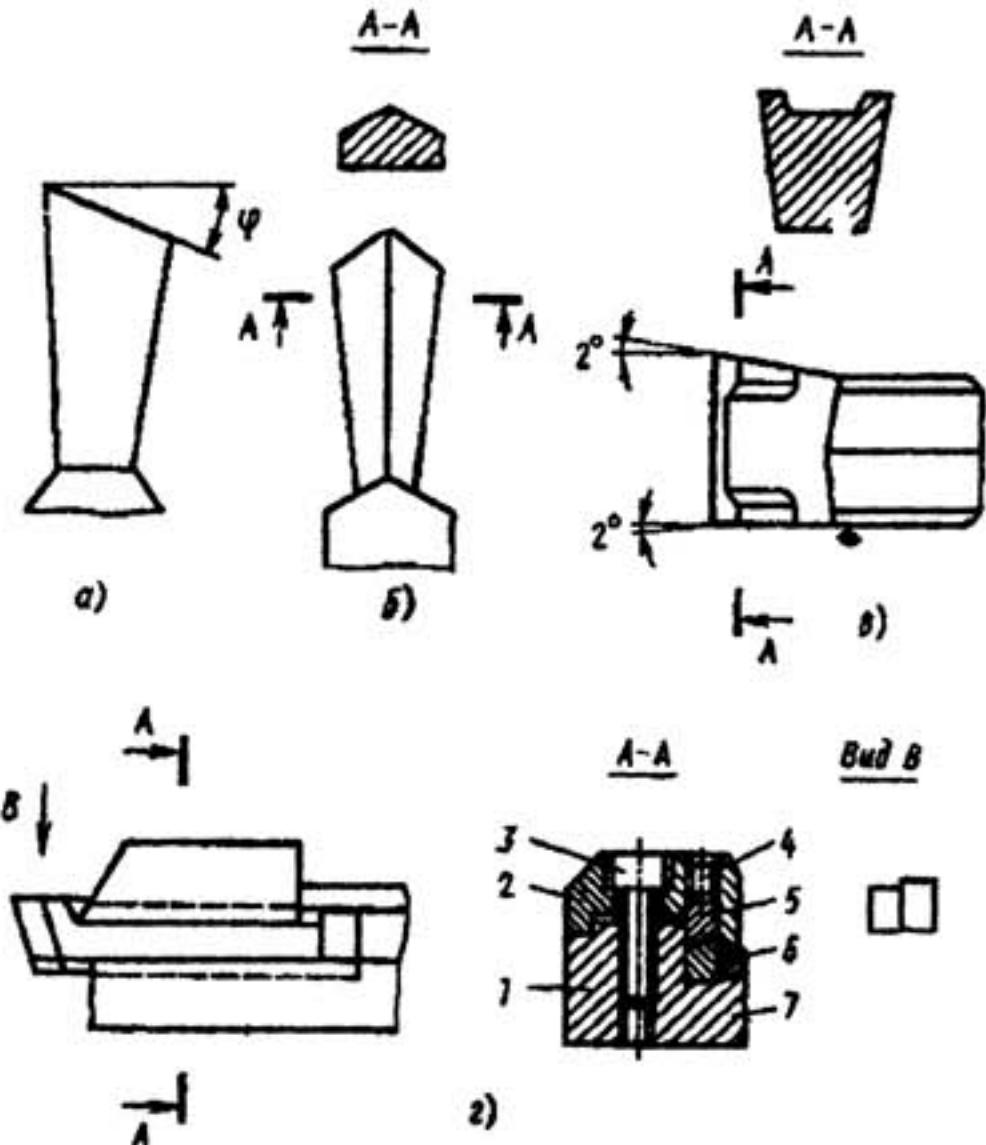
Конструкция отрезных резцов с различной формой режущих кромок:
